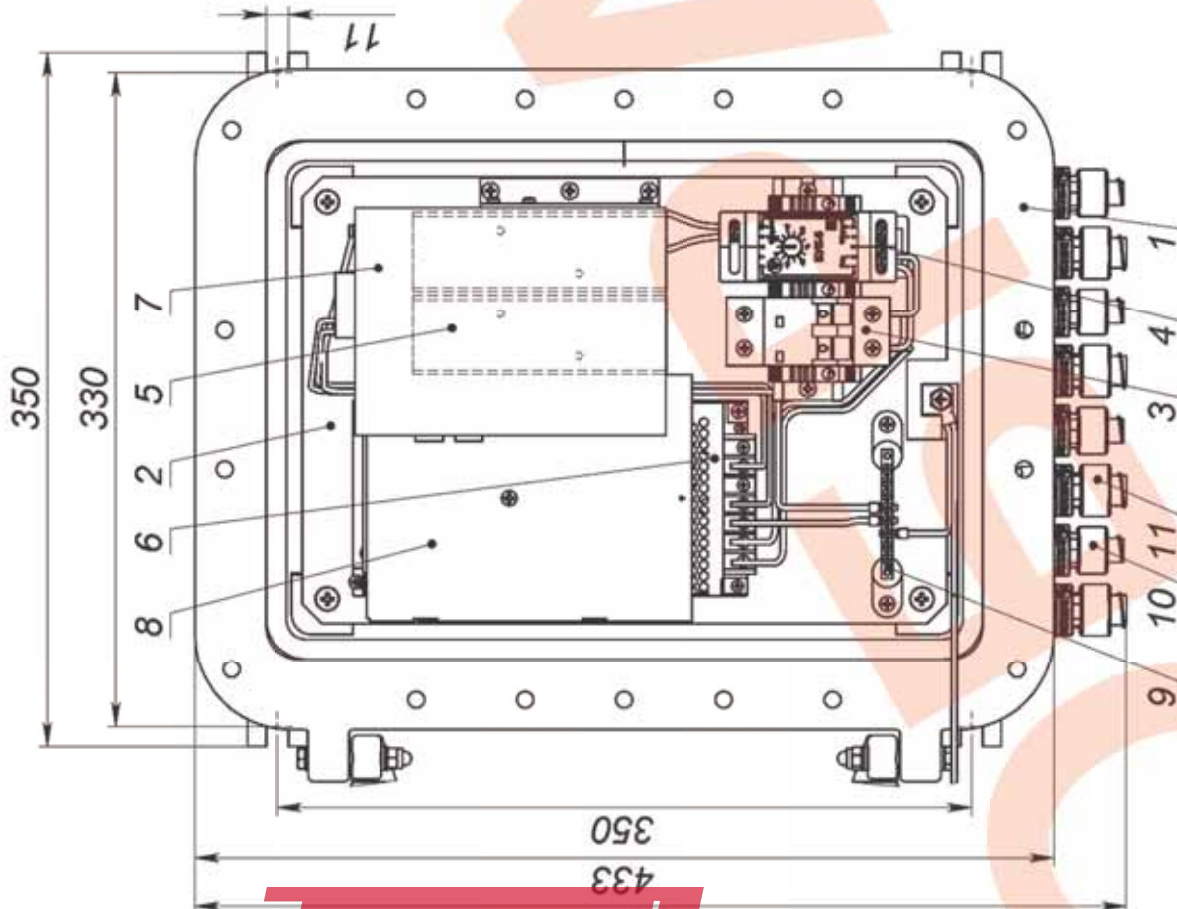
Устройство и габаритно-установочные размеры (крышка не показана)
